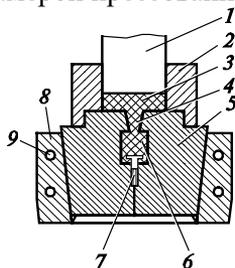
Рабочая часть пресс-формы для литьевого прессования с верхней камерой прессования:
